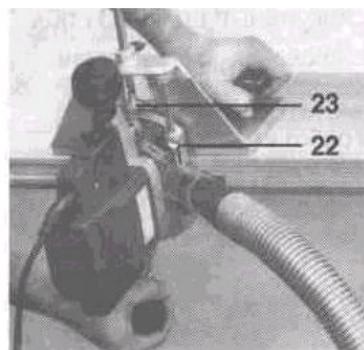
Фрезерование паза на торце доски. Фрезерная машина с угловым упором 30 103.
